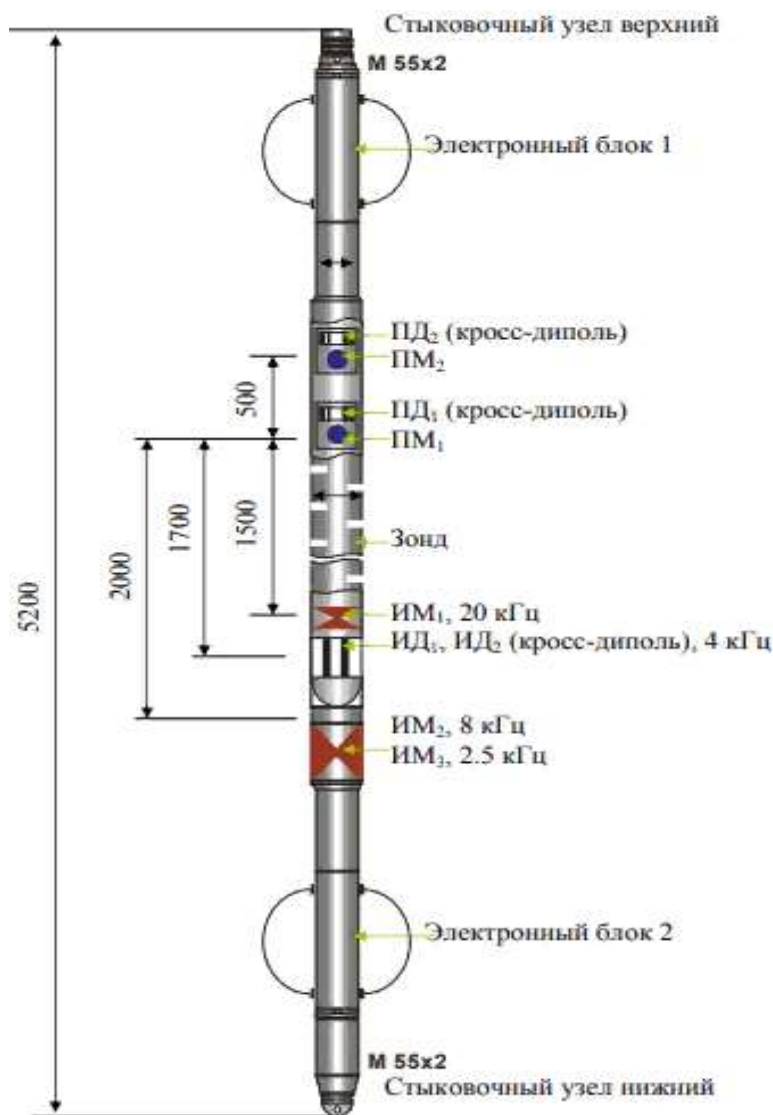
Схематичный чертёж общего вида скважинного прибора АВАК-11.
